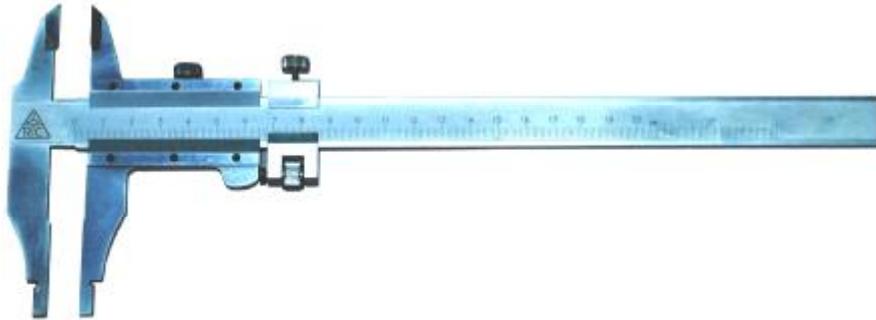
Общий вид штангенциркулей типа ШЦ-II
